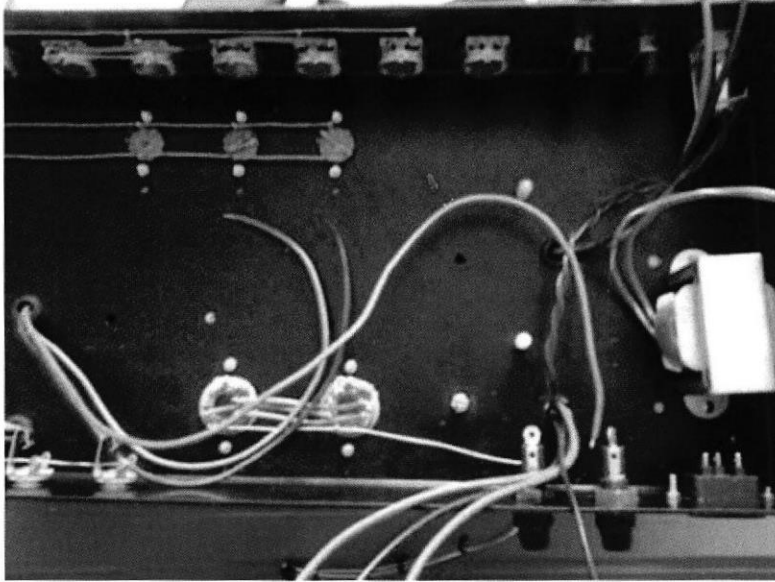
Montaje y cableado de potenciómetros, sockets, choke y transformadores.
